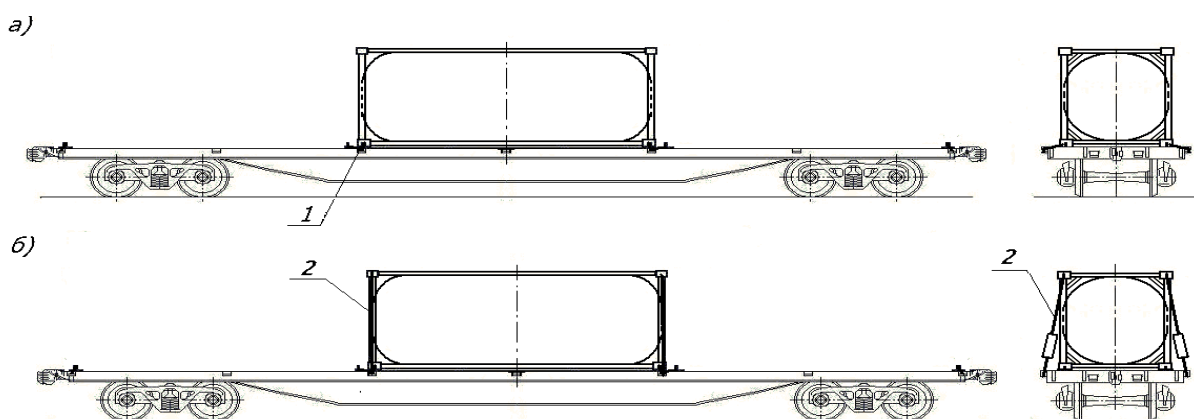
Дополнительное крепление контейнера-цистерны на платформе для крупнотоннажных контейнеров:
